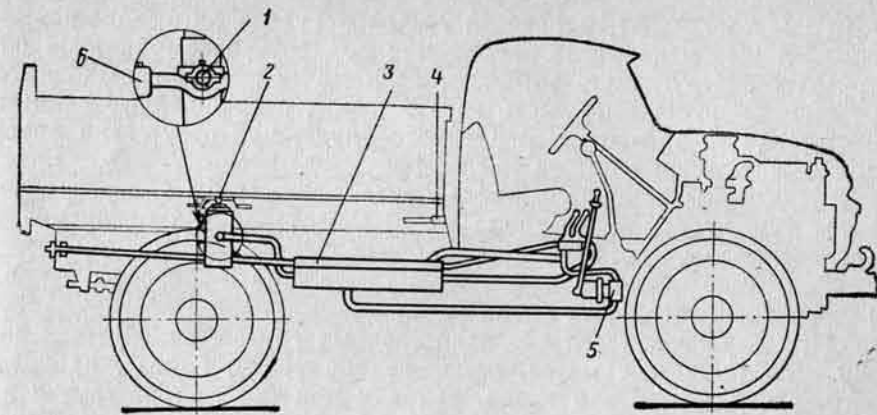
Схема смазки самосвального оборудования автомобиля-самосвала ЗИЛ-ММЗ-554
